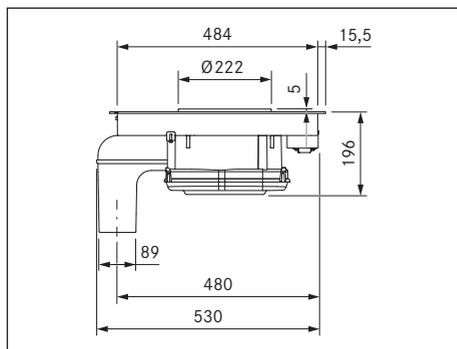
BHA dimensioni apparecchio vista laterale
